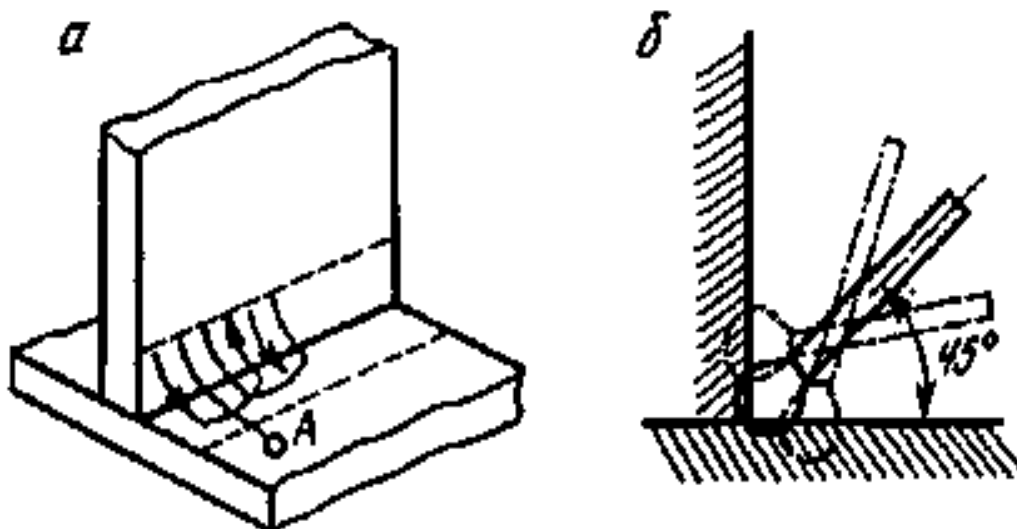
Схема колебательных движений электродом при однослойной сварке угловых швов: *a* – траектория движения конца электрода; *б* – изменение угла наклона электрода; *A* – точка начала сварки
